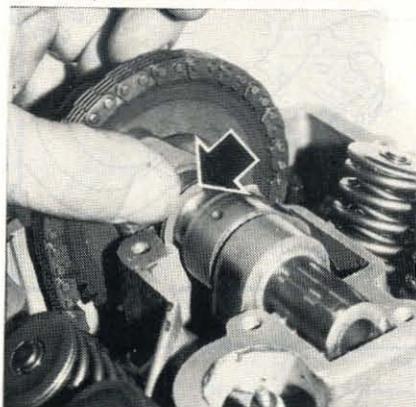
Demi-segment de calage latéral (Photo RMT)
